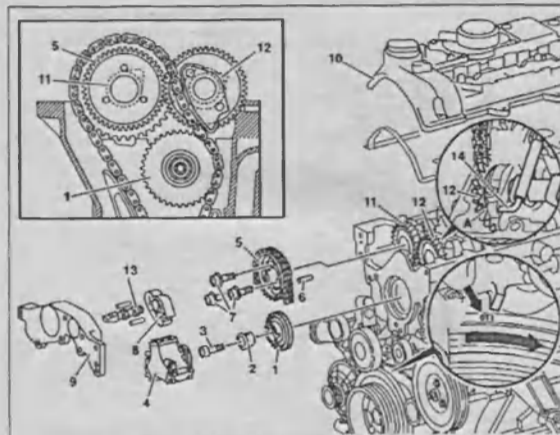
Снятие и установка промежуточной шестерни привода ТНВД:
